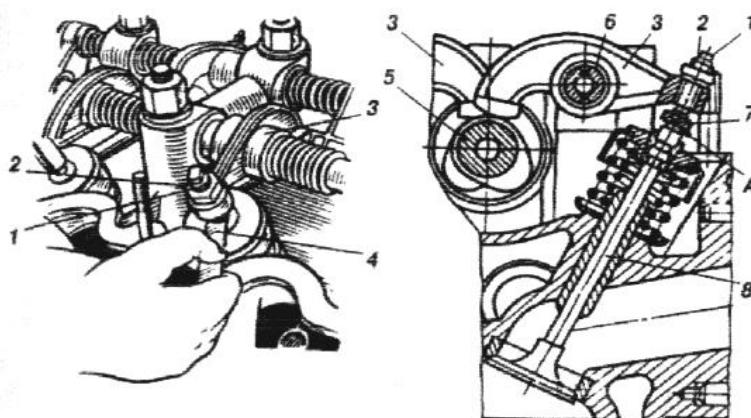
Проверка и регулировка тепловых зазоров в механизме привода клапанов двигателя УЗАМ 331.10: 1 -регулировочный винт; 2 – контргайка регулировочного винта; 3 - коромысло, 4 - плоский щуп; 5 - распределительный вал; 6 - ось коромысел; 7 - наконечник регулировочного винта; В – клапан; А - тепловой зазор.
